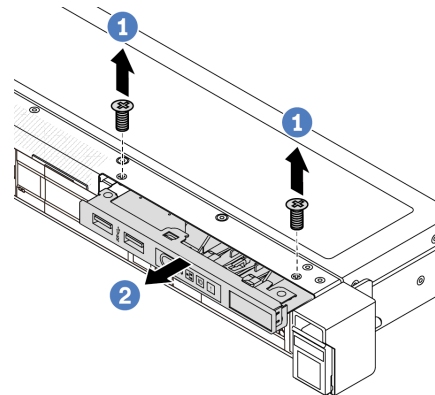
Remover um módulo de E/S frontal no chassi de 3,5 pol.
